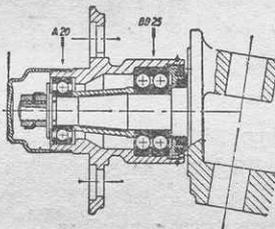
Ступица переднего колеса на шарикоподшипниках.
